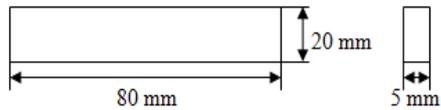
Dimensi Spesimen Uji Impact JIS Z 2202
